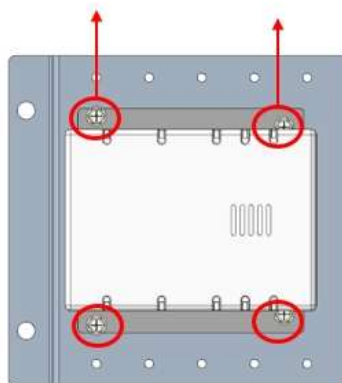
Remova os parafusos de fixação do detetor de gás combustível
